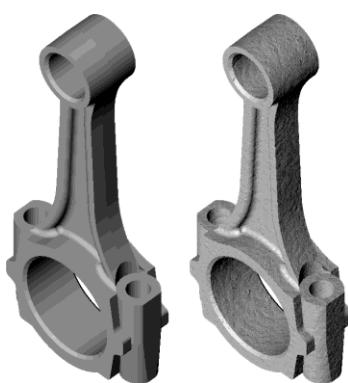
Твердотільна модель шатуна (SolidWorks)
